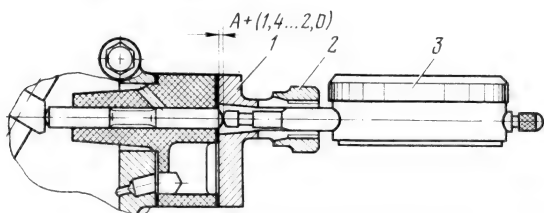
Приспособление для замера выступления штанги привода бензонасоса:
